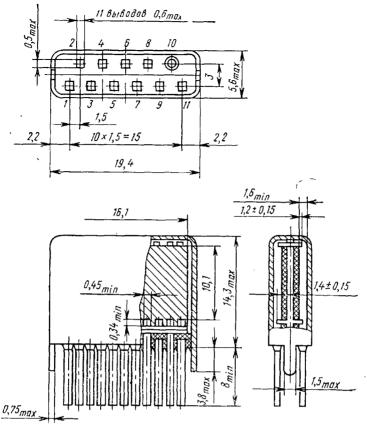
Конструкция металлополимерного корпуса «Акция»
